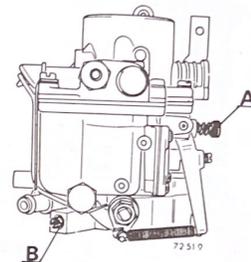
Vista del carburador Solex 32 EISA-2, referencia 473, enseñando los tornillos del reglaje del ralentí.
